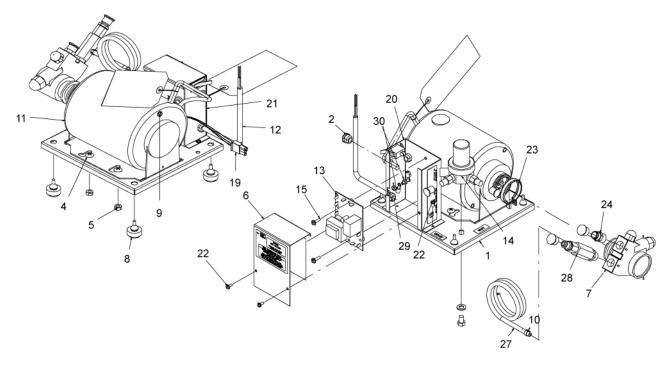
COMPOSIÇÃO BOMBA E MOTOR
